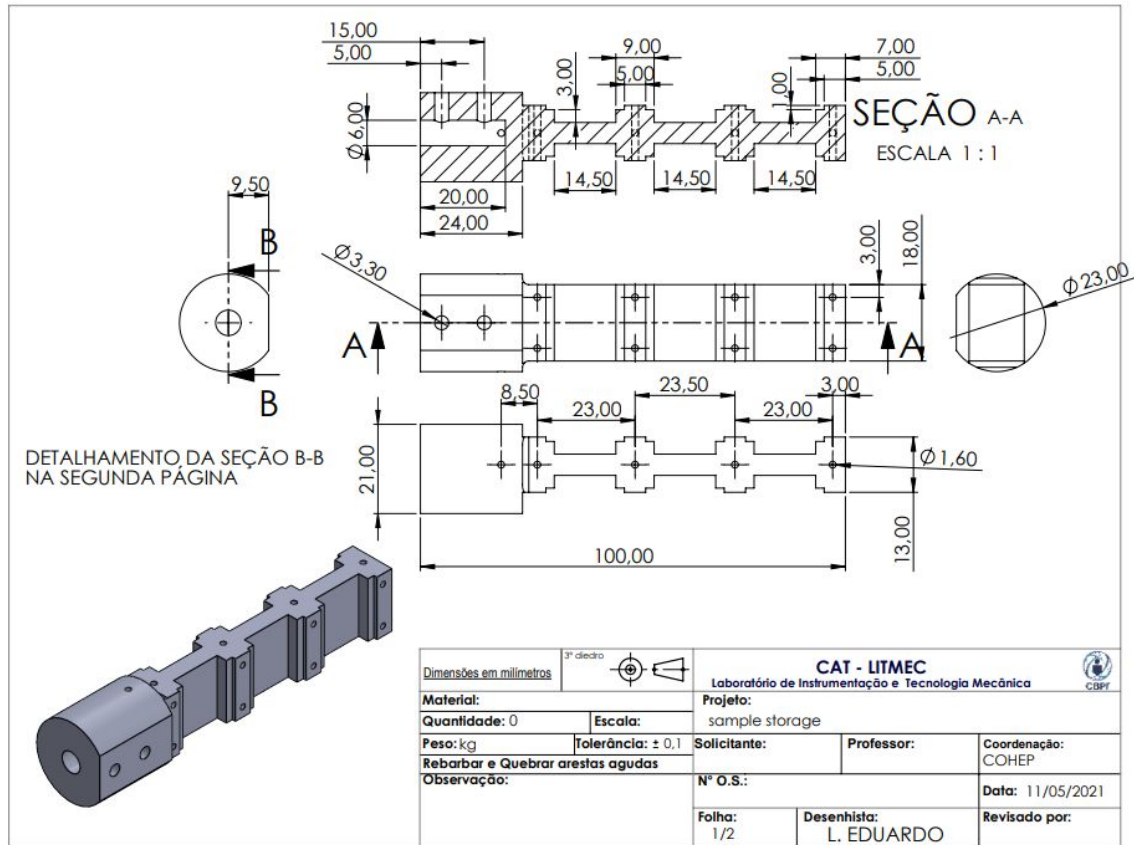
Desenho técnico para fabricação de Sample Storage. Fonte: LITMEC, 2022.
